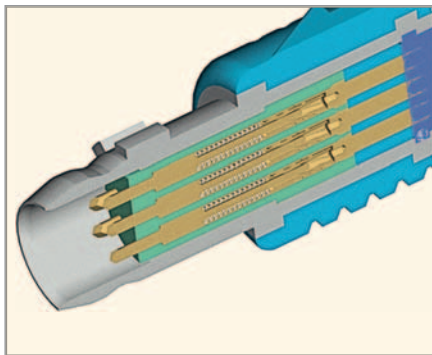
Цилиндрический соединитель серии SnapTas в разрезе
